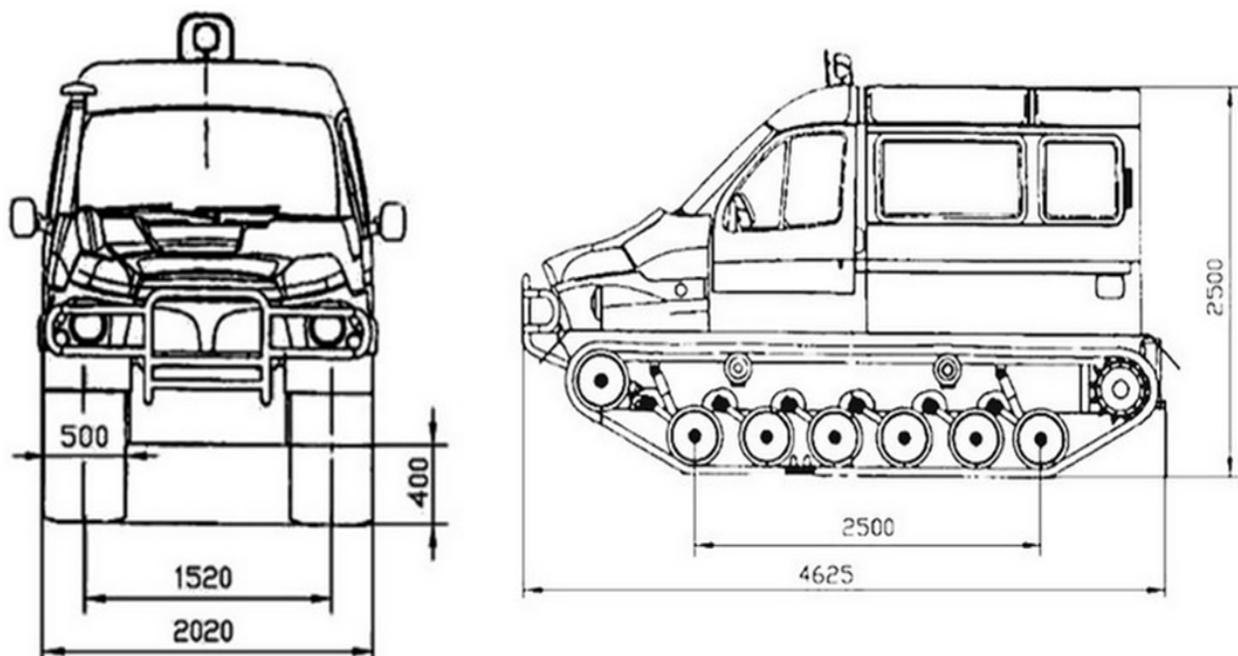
Габаритные размеры ГАЗ-3409 "Бобр"
